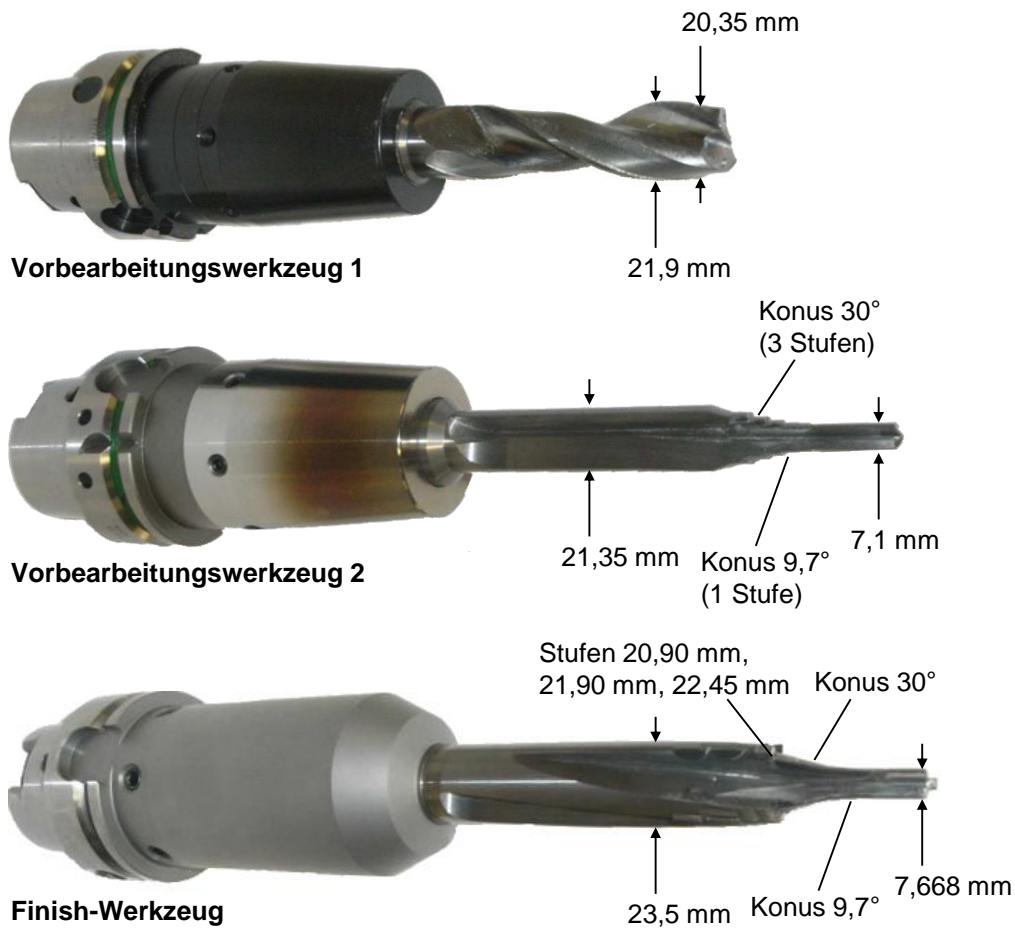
Finaler Stand der MMS-Werkzeuge zur Bearbeitung der Injektorbohrung im ZK N20
